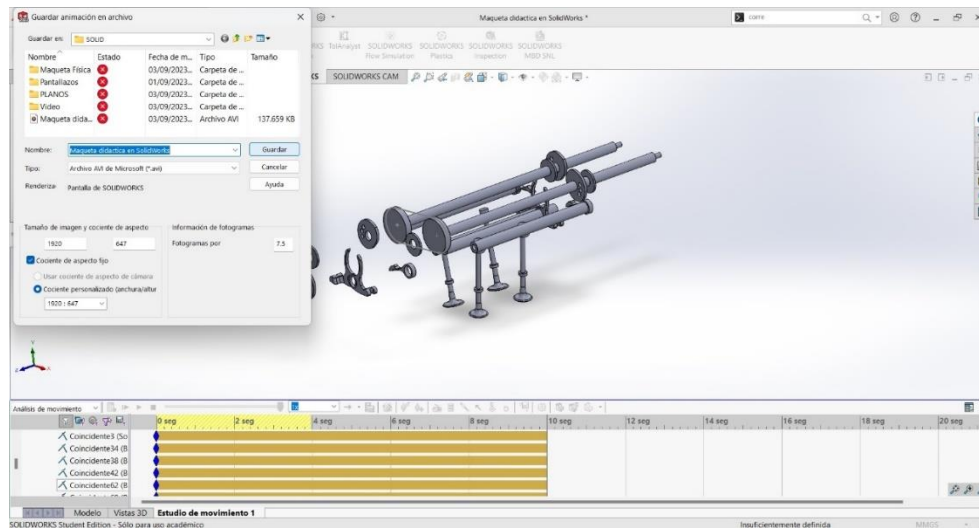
Salvar video de Explosionado. Fuente: SolidWorks
